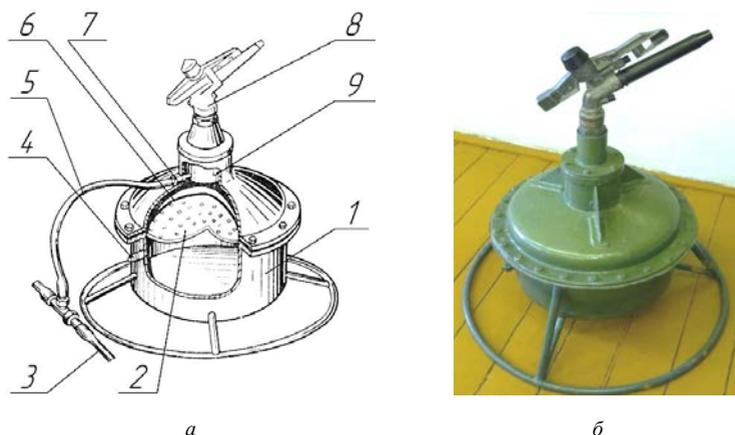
Импульсный дождеватель: *а* – схема; *б* – общий вид; 1 – гидроаккумулятор; 2 – свод; 3 – поливной трубопровод; 4 – штуцер для заполнения гидроаккумулятора воздухом; 5 – шланг; 6 – эластичная мембрана; 7 – присоединительный штуцер; 8 – дождевательный аппарат; 9 – запорный орган
